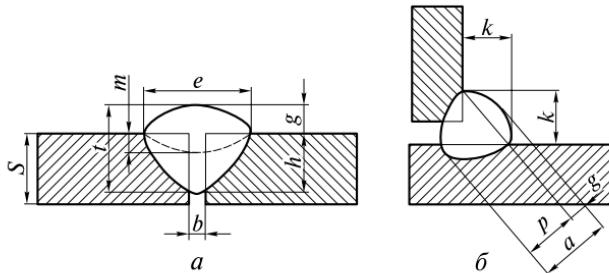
Основные геометрические параметры стыкового (а) и углового (б) сварных швов:
